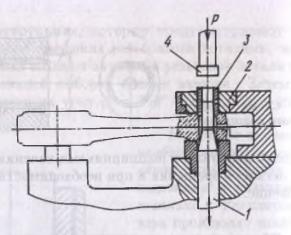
Схема запрессовки втулки: 1, 2 — направляющие элементы; 3 — втулка; 4 — шток пресса
